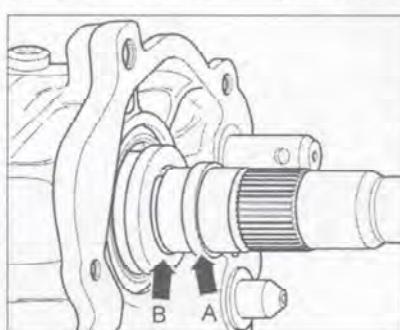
Установите фрикционное кольцо (стрелка А) игольчатого подшипника шестерни 6-й передачи. Буртик должен быть направлен в сторону стопорного кольца (стрелка В).
